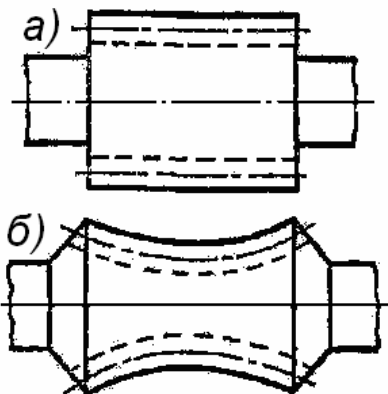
Циліндричний (а) і глобоїдний (б) черв'яки
